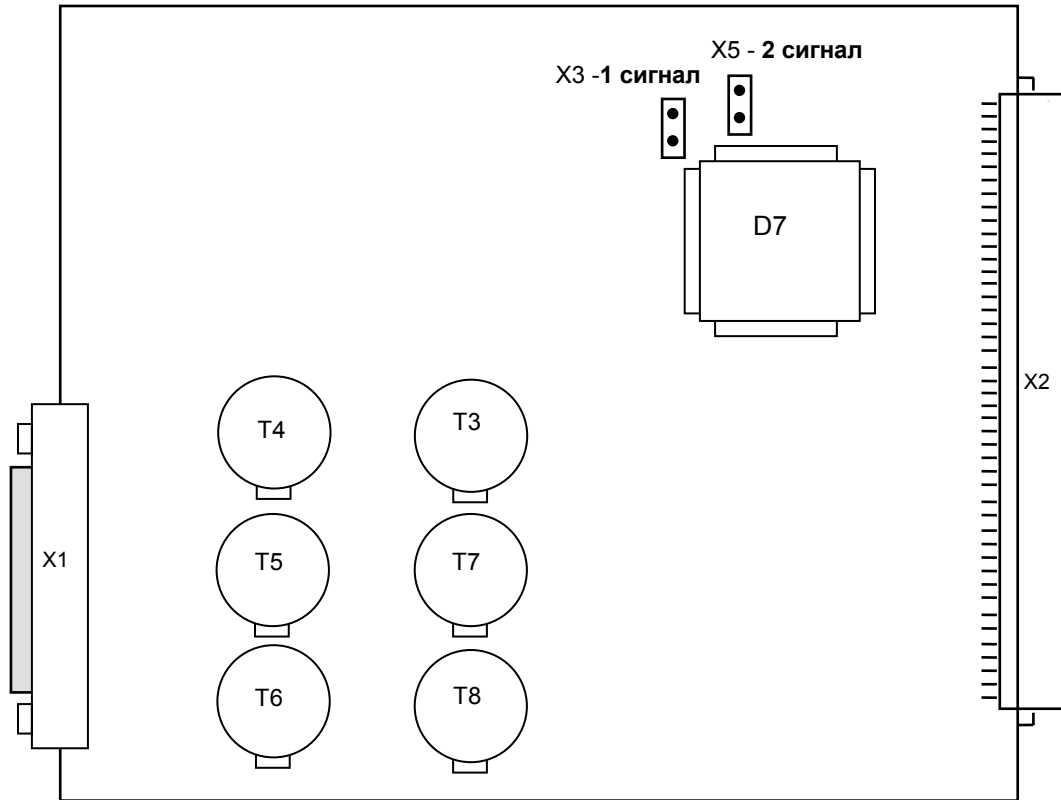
Расположение соединителей штыревых на печатной плате ячейки ОЦСД
